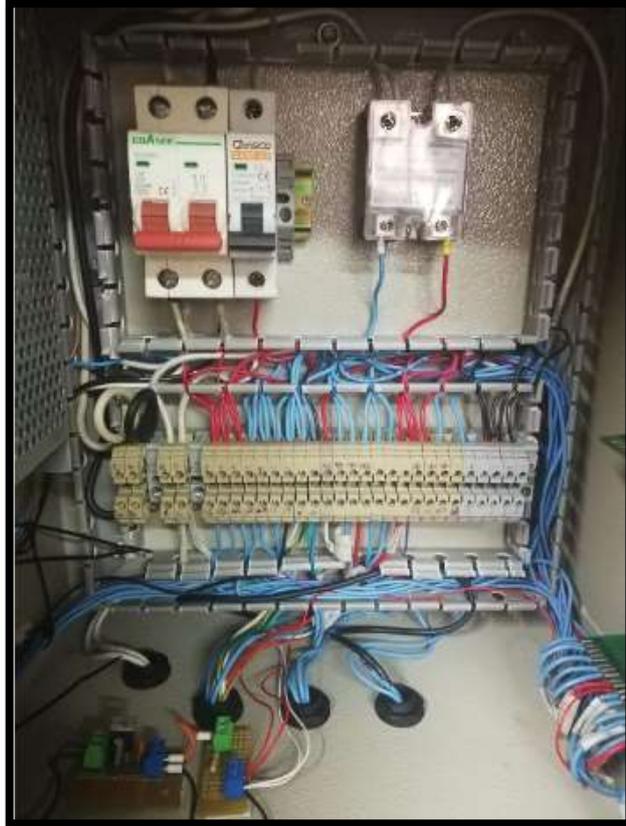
Cableado de la parte interna del tablero de control para la planta.
